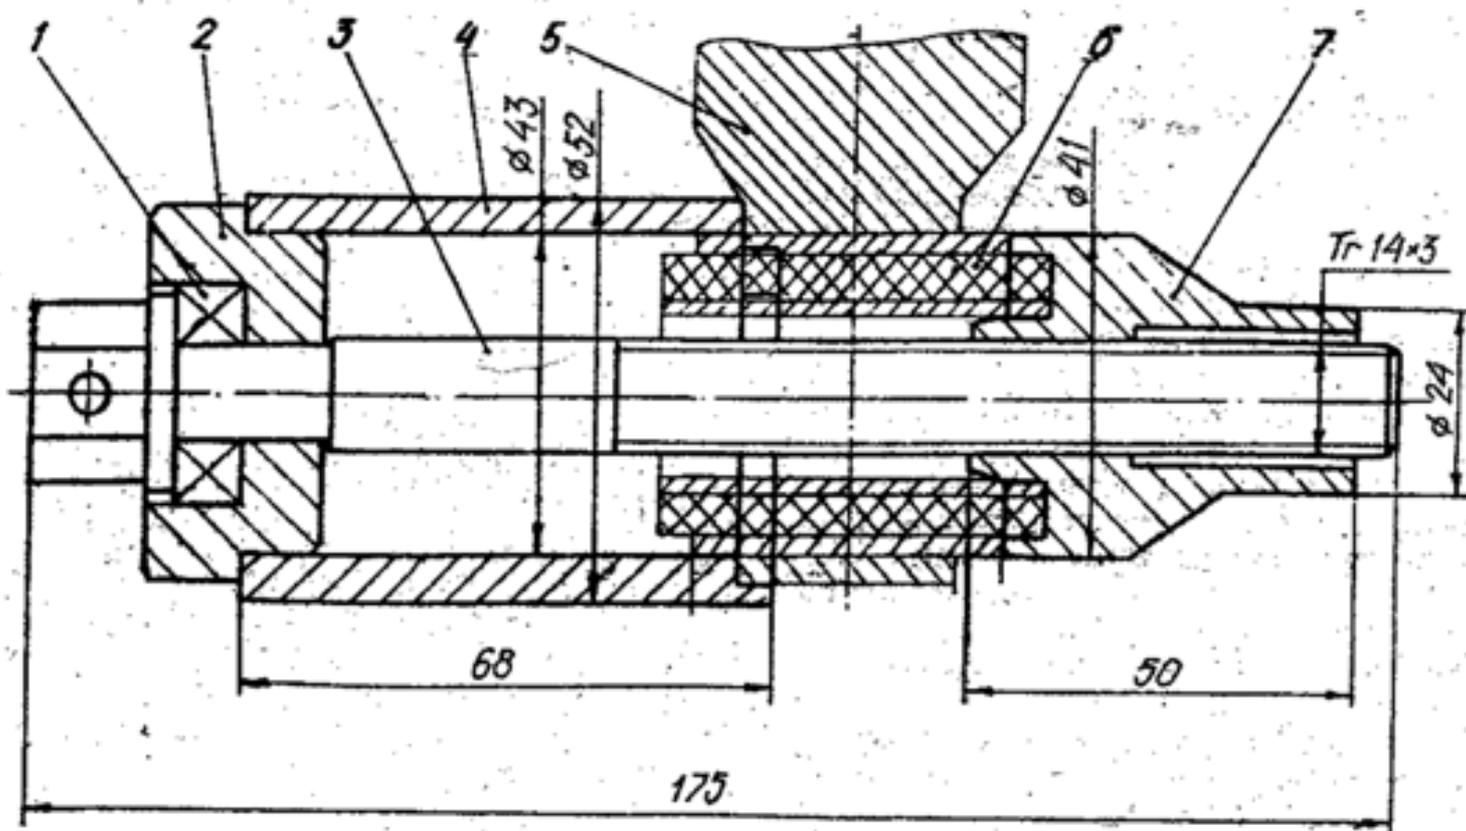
Запрессовка и выпрессовка сайлентблока амортизатора задней подвески: 1 - подшипник; 2 - корпус подшипника; 3 - винт; 4 - стакан; 5 - амортизатор; 6 - сайлентблок; 7 - толкатель.
